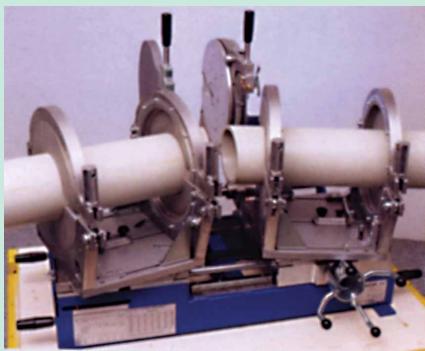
аппарат для стыковой сварки трубопроводов из ПВДФ.
